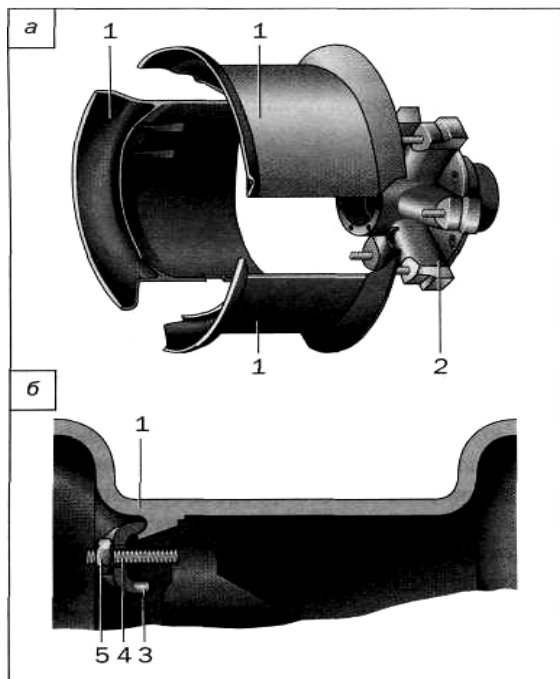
Бездисковое колесо, его общий вид (а) и крепление колеса (б): 1 — секторы колеса; 2 — ступица; 3 — крепление; 4 — шпилька; 5 — гайка
